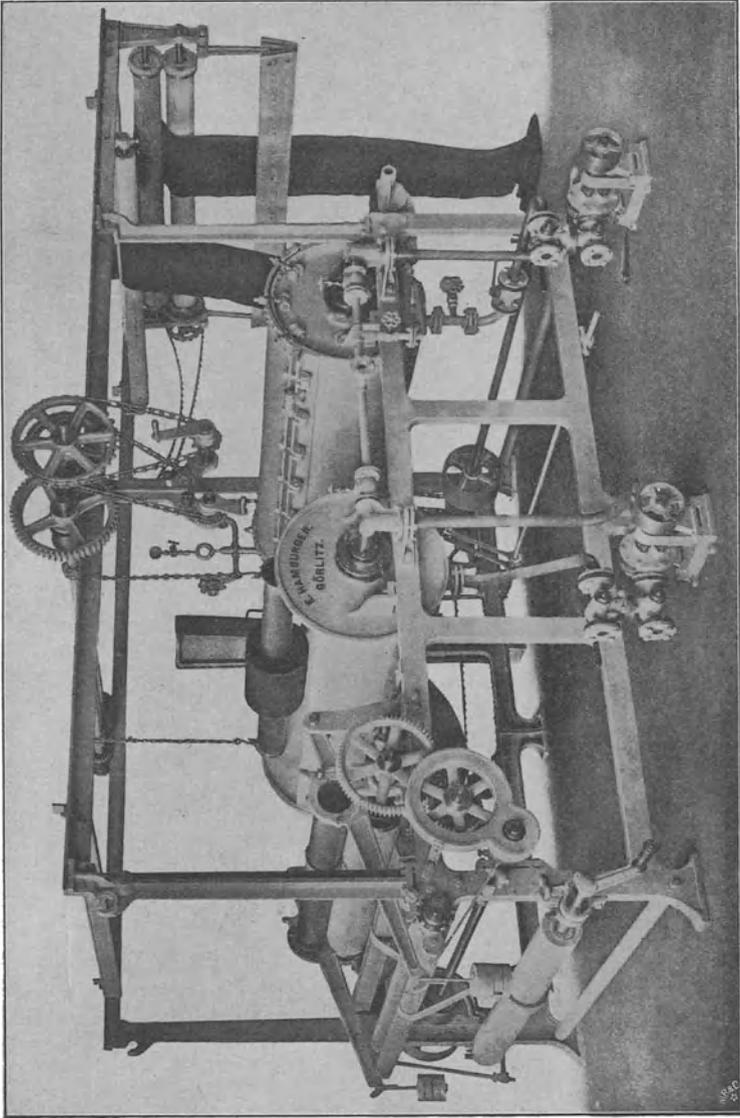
Universal-Doppeldekatiemaschine von Hamburger.
